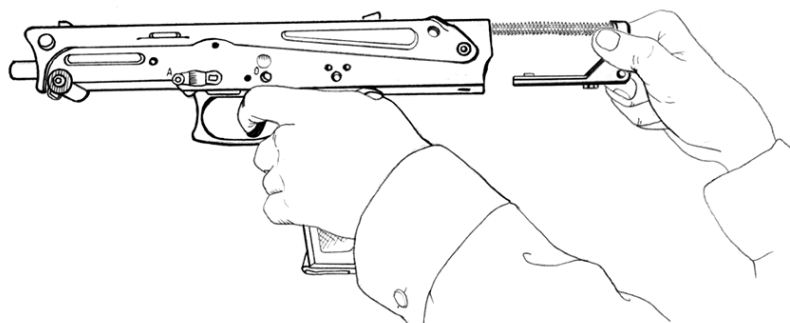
Постановка корпуса затыльника в коробку автоматики
